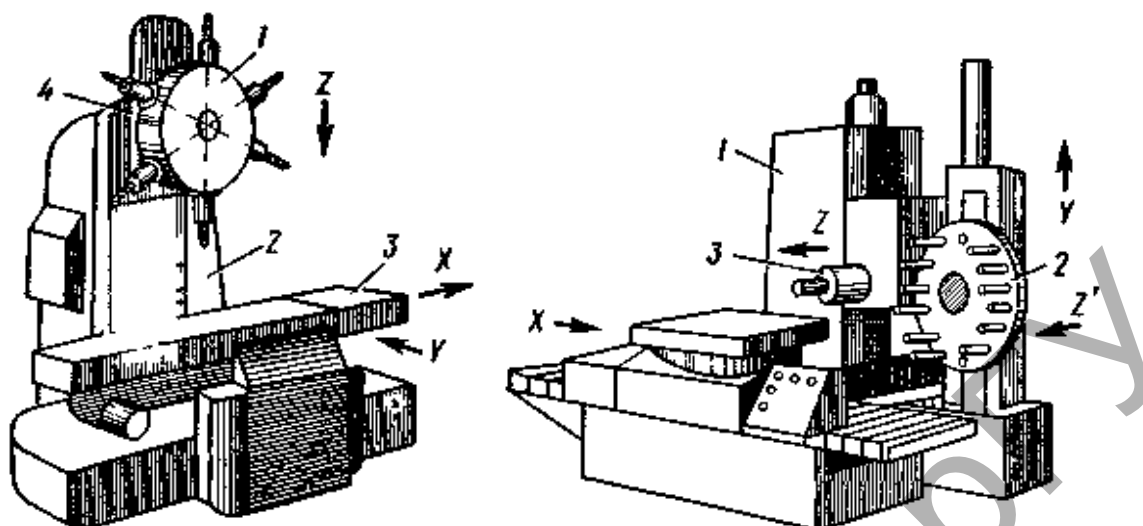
Компоновка многооперационных станков на базе вертикально-фрезерного станка с револьверной головкой и горизонтально-расточного станка с магазином инструментов
